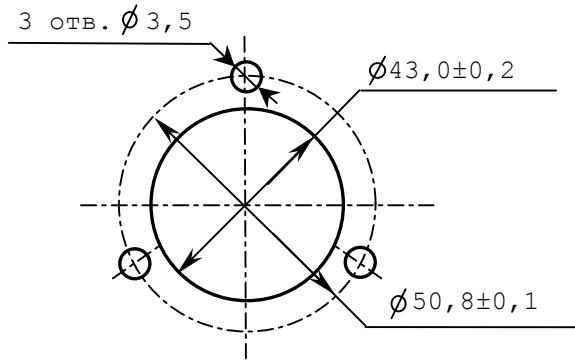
Установочные размеры штурвала ZBG-5-003-100
